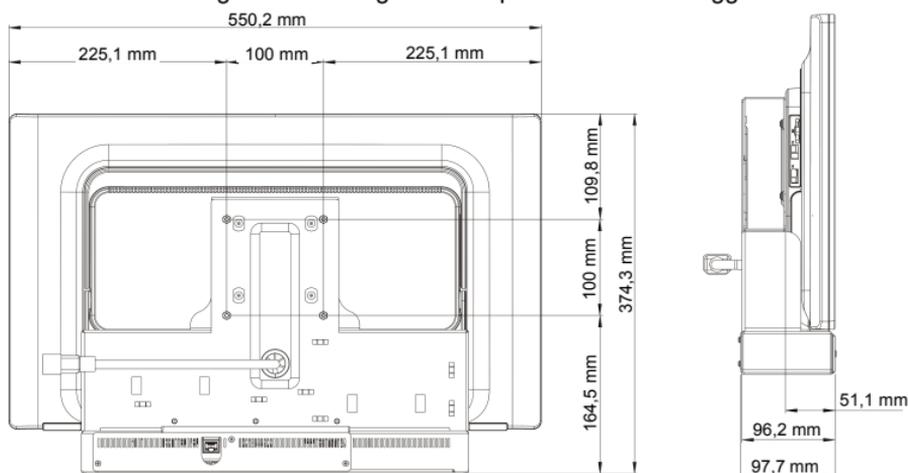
Dimensioni di montaggio del sistema CC5000-22
